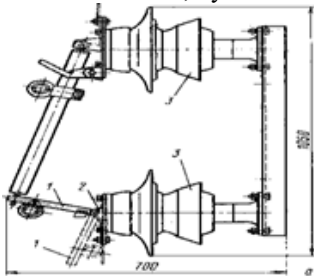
Предохранитель типа ПКТ: 1-цоколь; 2-опорный изолятор; 3-контакт; 4-патрон; 5-замок
